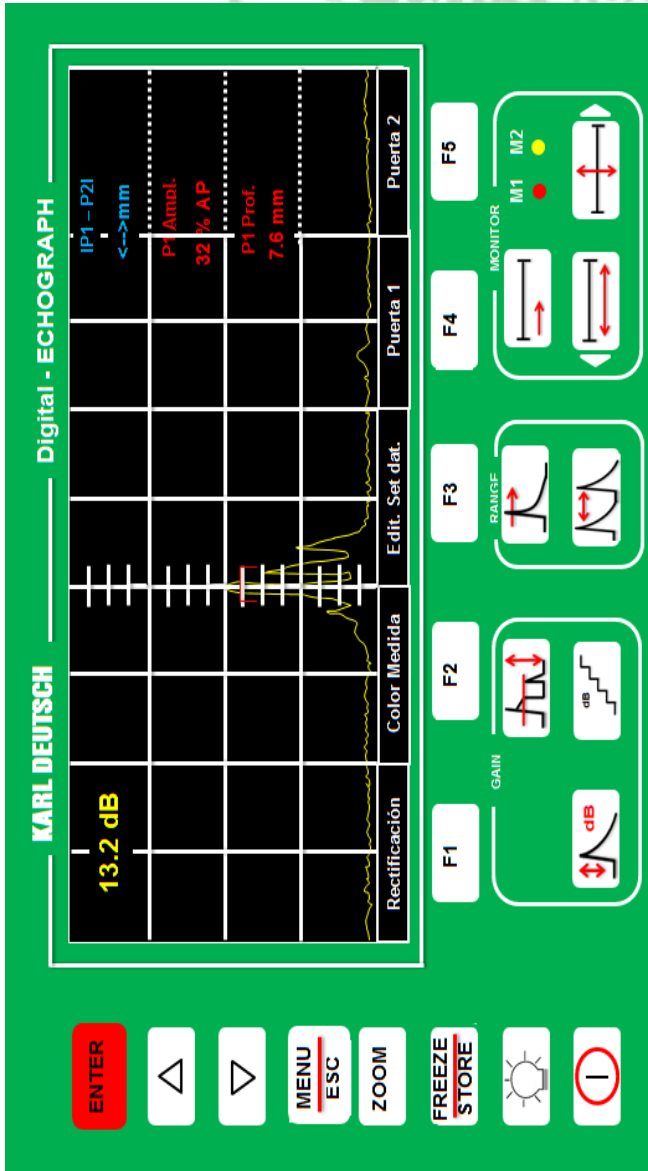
Pantalla de Inspección 1 lado izquierdo
